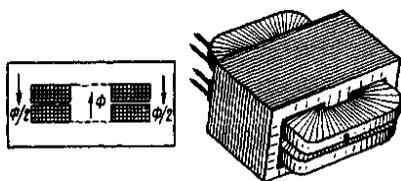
Однофазный трансформатор броневоего типа: а- устройство; б- внешний вид
